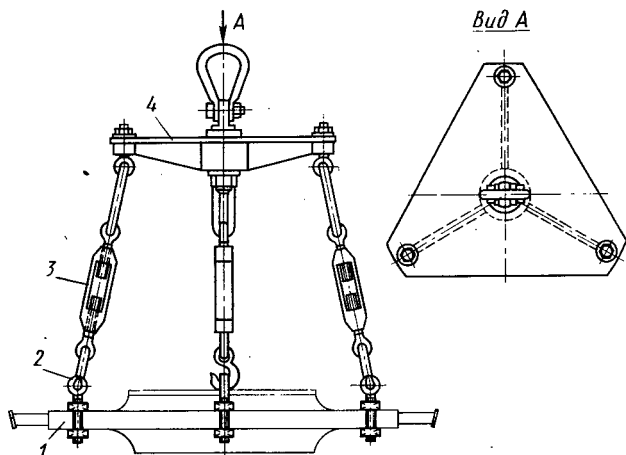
Приспособление для подъема рабочих колес (дисков) при насадке их на вал:
